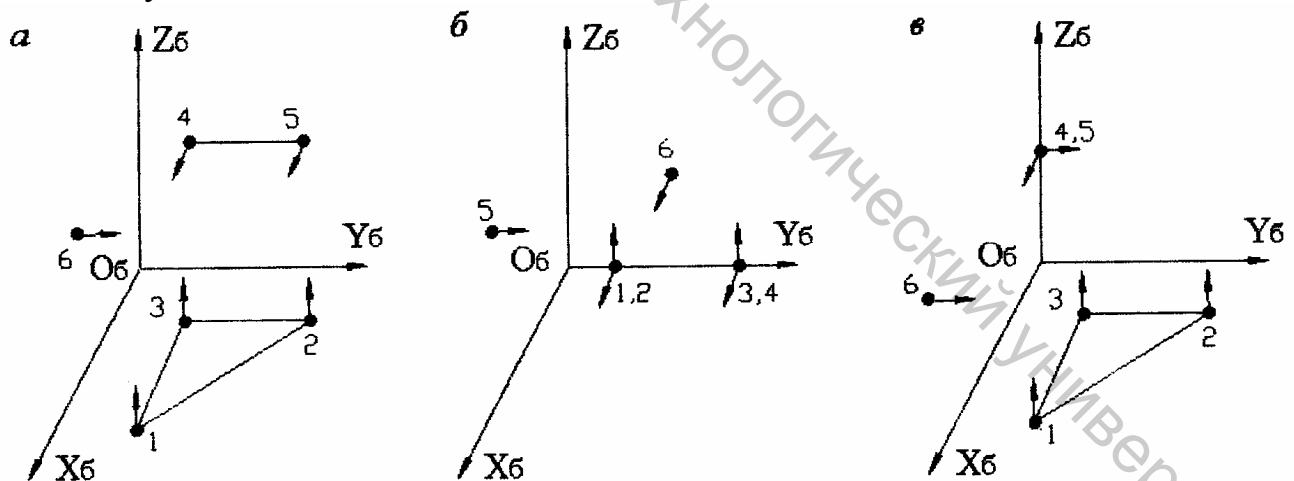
Примеры расположения точек сопряжения в базовой системе координат
